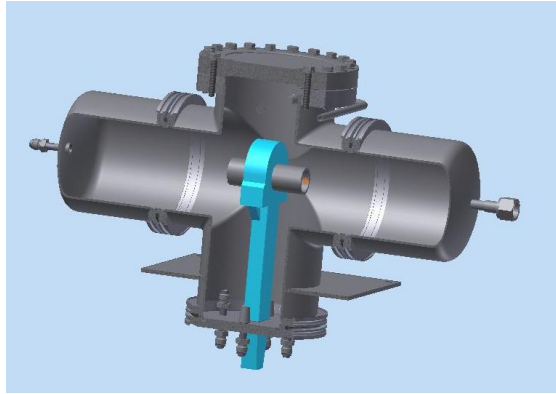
Verteiler mittels WIG-Innenorbitalschweißtechnik
